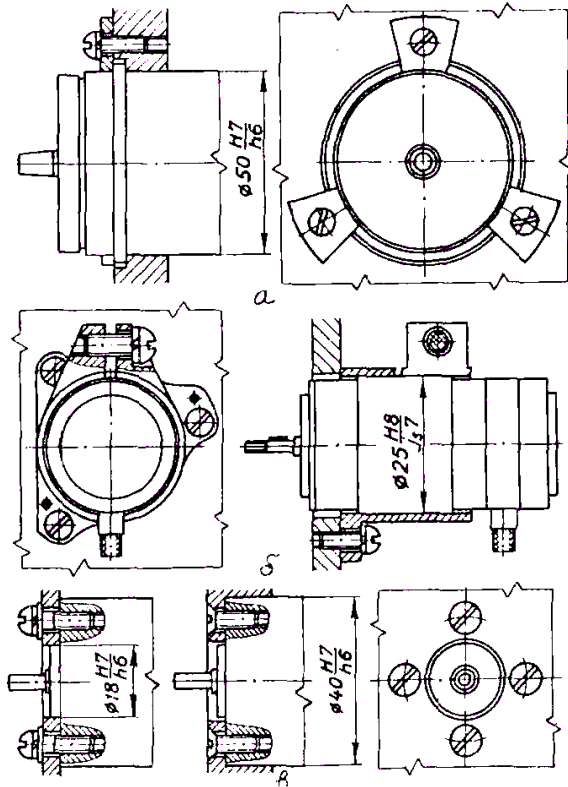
Способи установки у корпусах механізмів РЕА електричних мікромашин з циліндричним корпусом:
